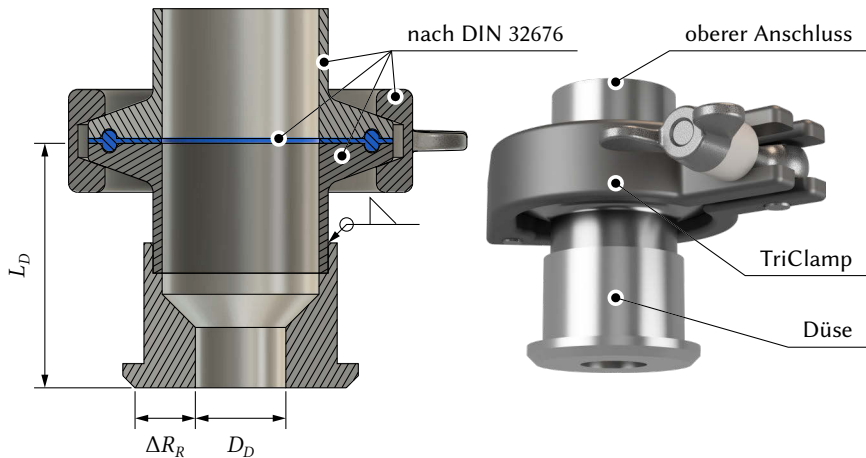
Werkzeugwechselsystem mit TriClamp-Klemmdichtung mit angeschlossener Düse
